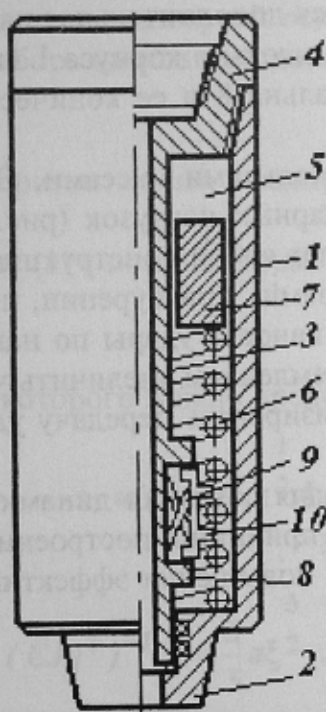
Устройство для создания ударных нагрузок на долото: 1 – корпус; 2, 4 – переводник; 3 – центральный патруб-бок; 5 – кольцевая пустота; 6 – пружина; 7 – груз; 8 – ограничительные бурты; 9 – пружина; 10 – центробежные отсекатели
